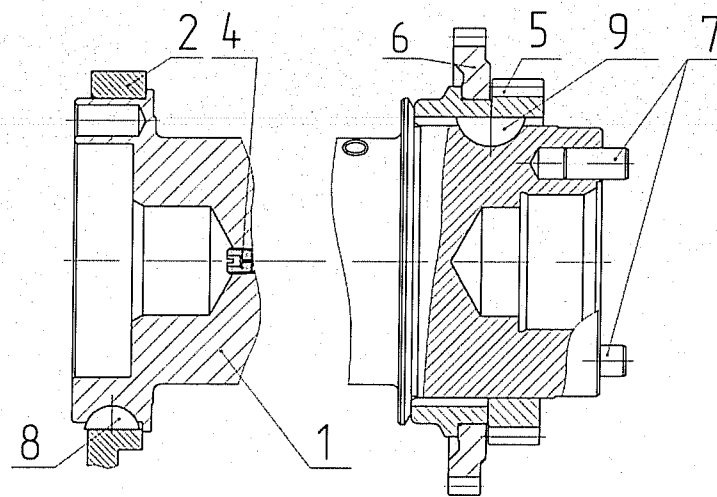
Сборочный чертеж коленчатого вала 7408.1005008-10, собранного на базе вала 740.13-1005020.
